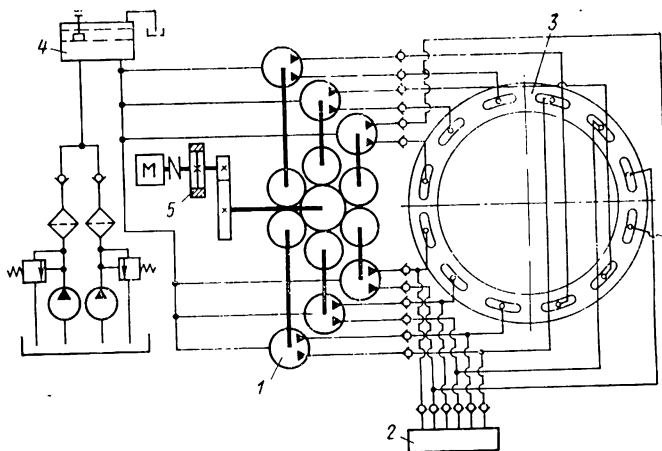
Схема гидростатической смазки насос — карман круговых направляющих планшайбы станков мод. КУ-322
